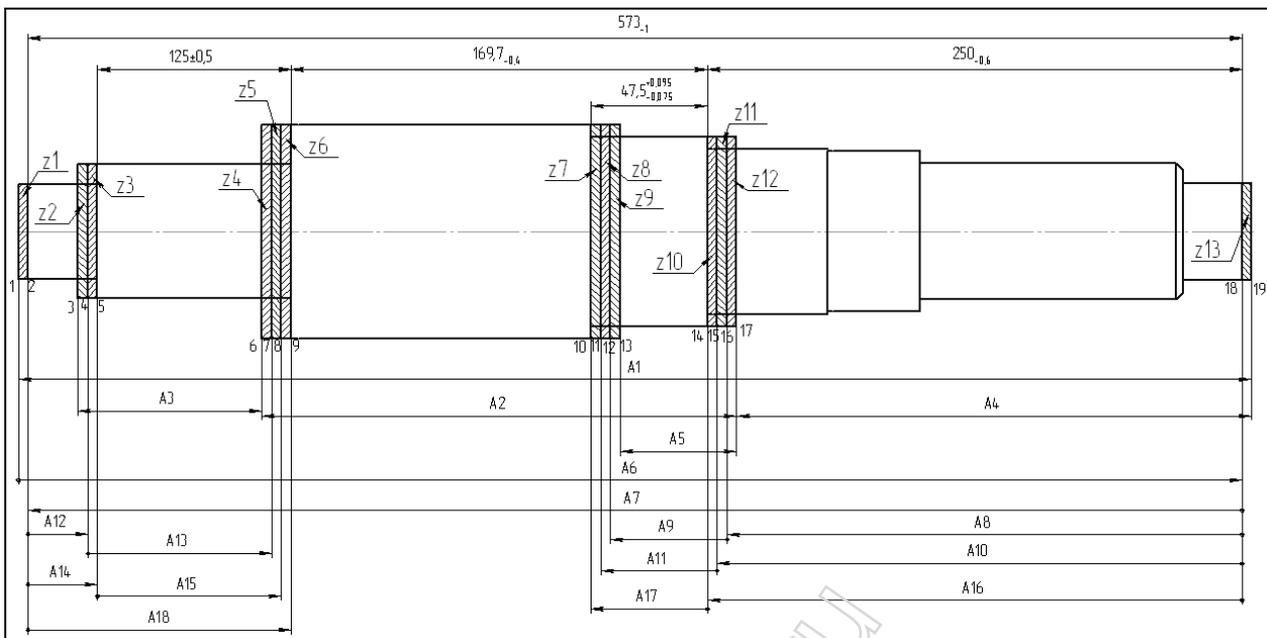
Размерная схема «Размерная схема.frw»
